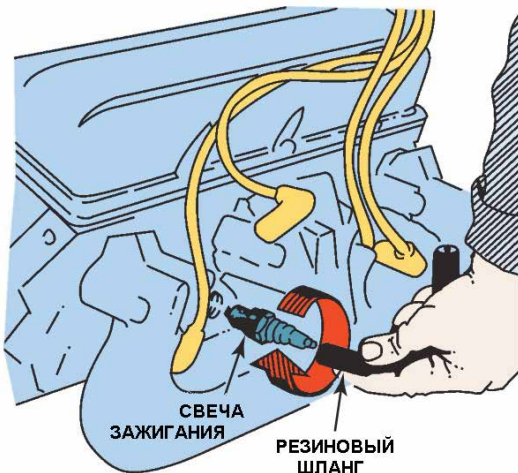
Используйте вакуумный или топливный шланг, надетый на изолятор свечи зажигания, чтобы установить свечу на её место без риска повреждения резьбы в свечном отверстии головки блока цилиндров; источник: Pearson Education, Inc.
